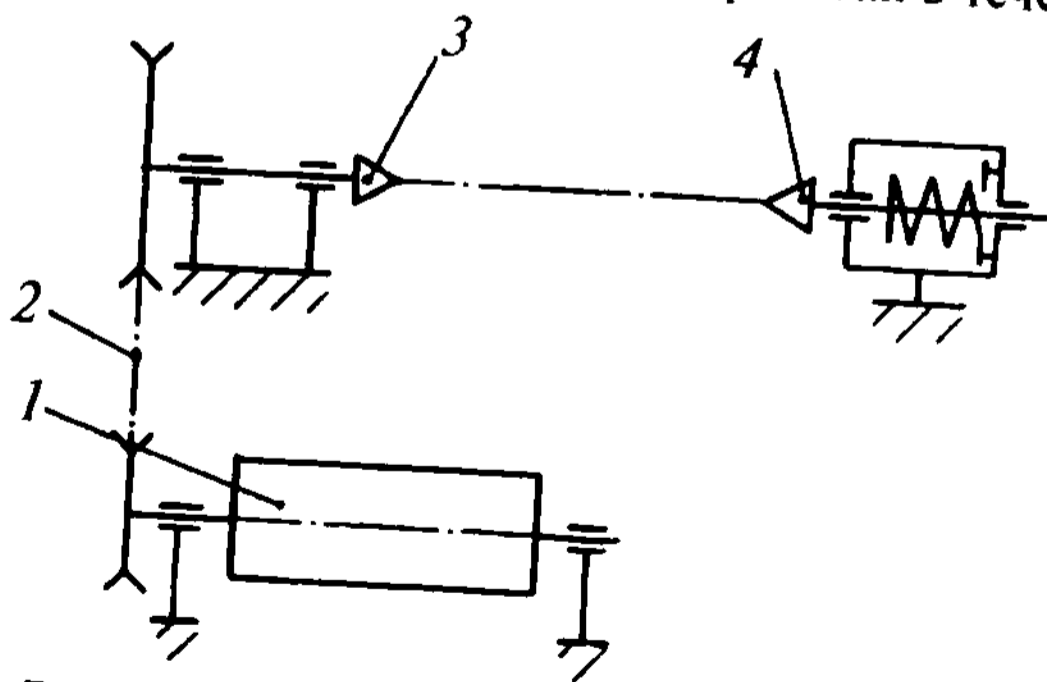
Схема станка для газопорошковой наплавки кулачков распределительного вала:
